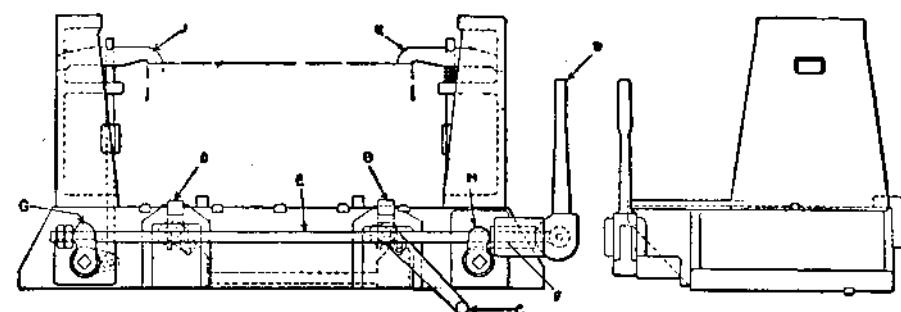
Приспособление Форда для закрепления блока при расточке.
